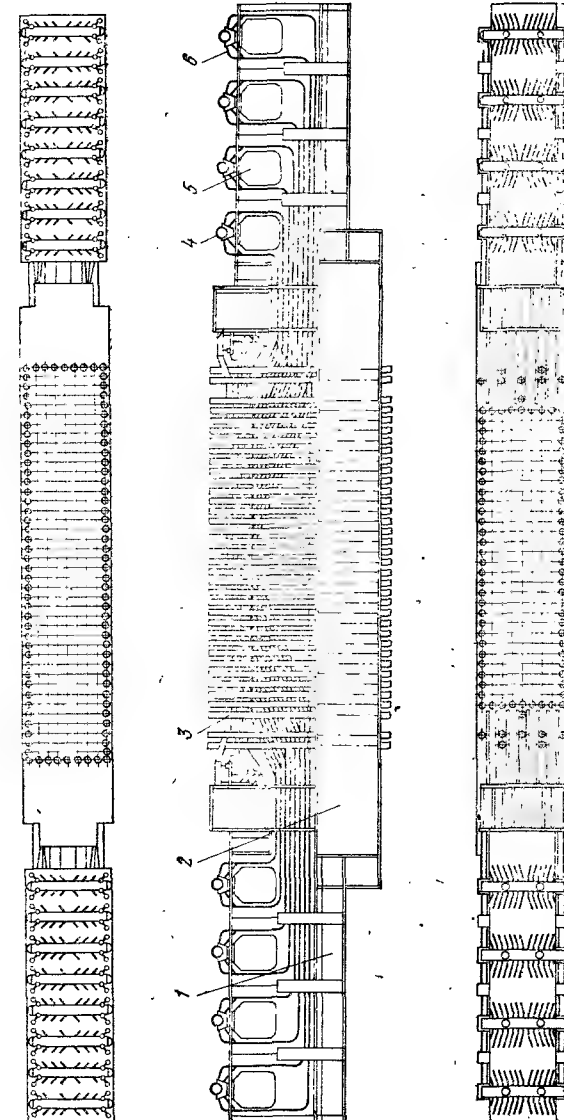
Верхний блок: 1 — консоль; 2 — металлоконструкция; 3 — стояк; 4 — сборный групповой коллектор; 5 — система КТО твэлов; 6 — индивидуальный трубопровод отвода теплоносителя
